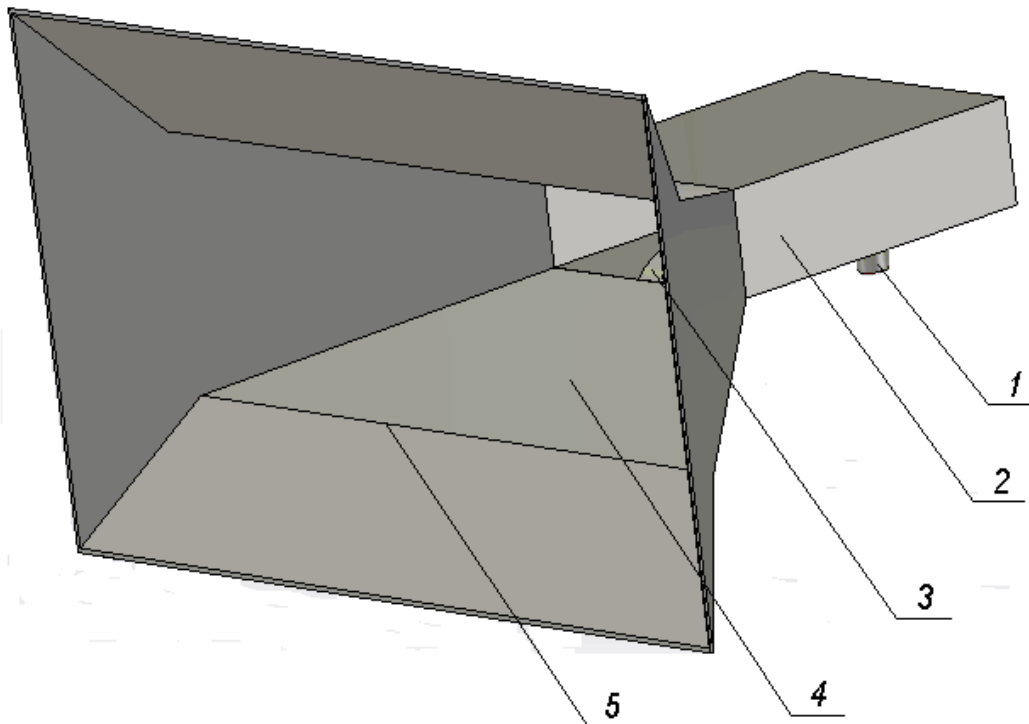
Общий вид рупора: 1 – коаксиальный порт; 2 – коаксиально-волноводный переход; 3 – гребень; 4 – рупор; 5 – излом стенки рупора
